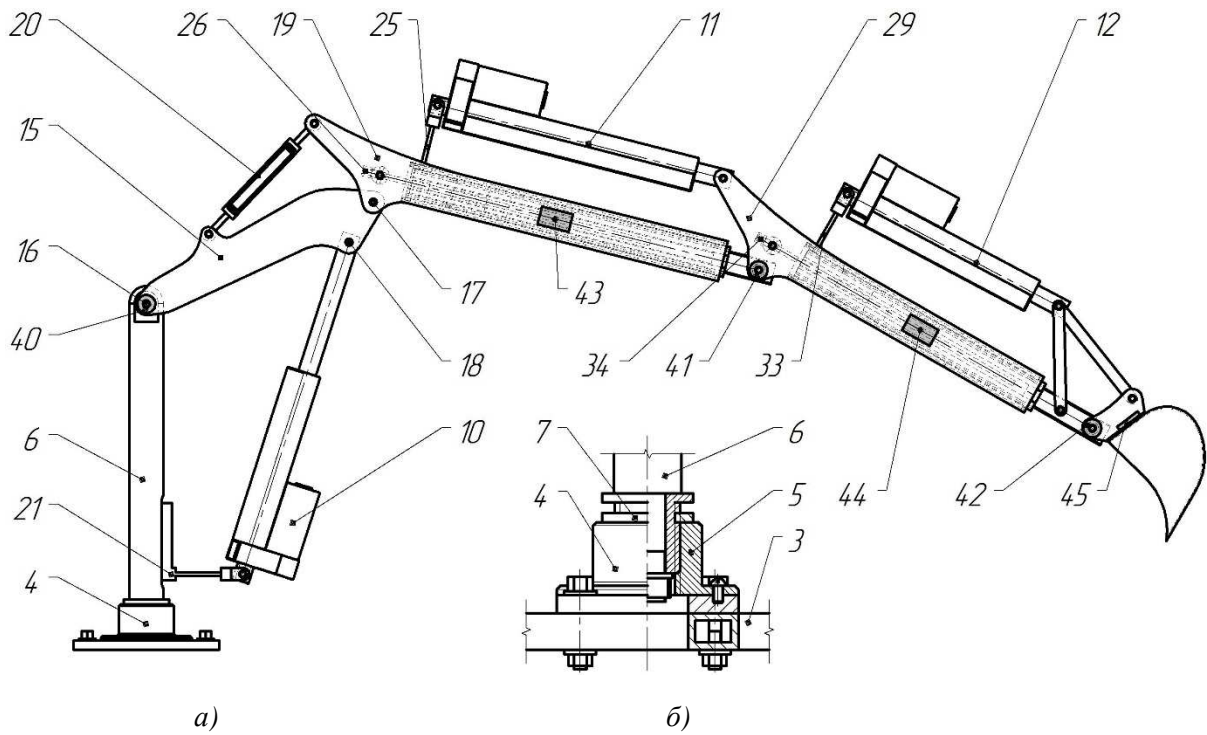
Фізична модель телескопічного робочого обладнання одноківшевого екскаватора: а) загальний вигляд; б) механізм обертання
